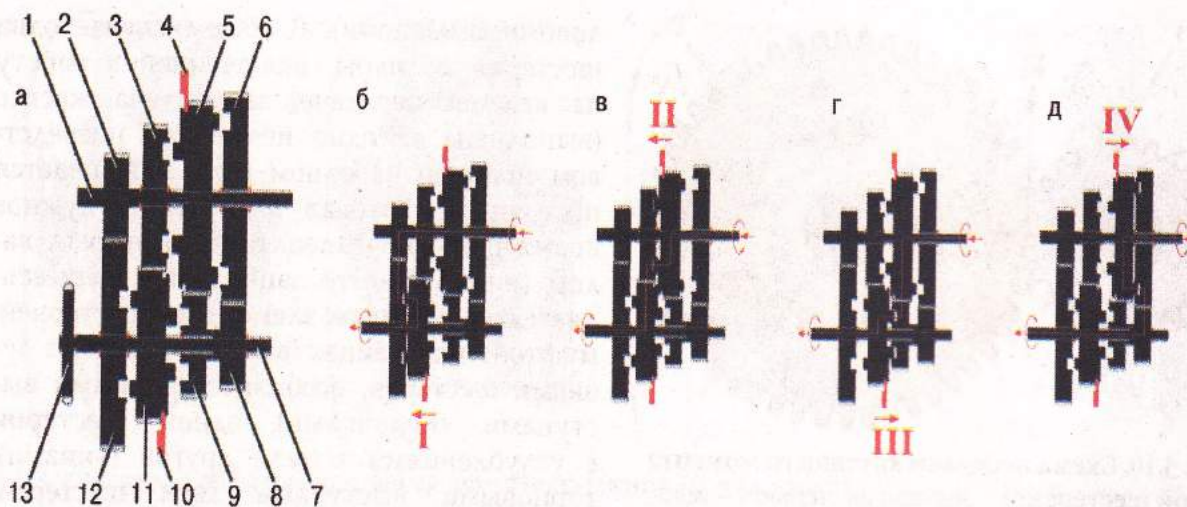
Схема двухвальной пятиступенчатой коробки передач: 1 – первичный вал; 2 – вторичный вал; 3 – ведущая звездочка вторичной передачи
